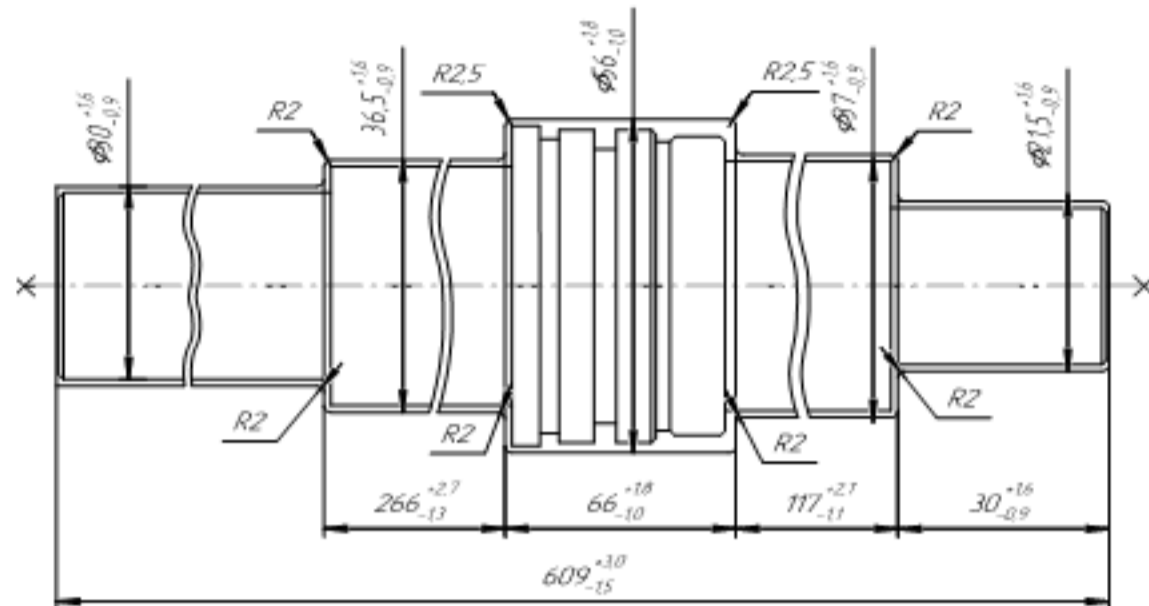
Ескіз заготовки, яка виготовляється на ГKM
